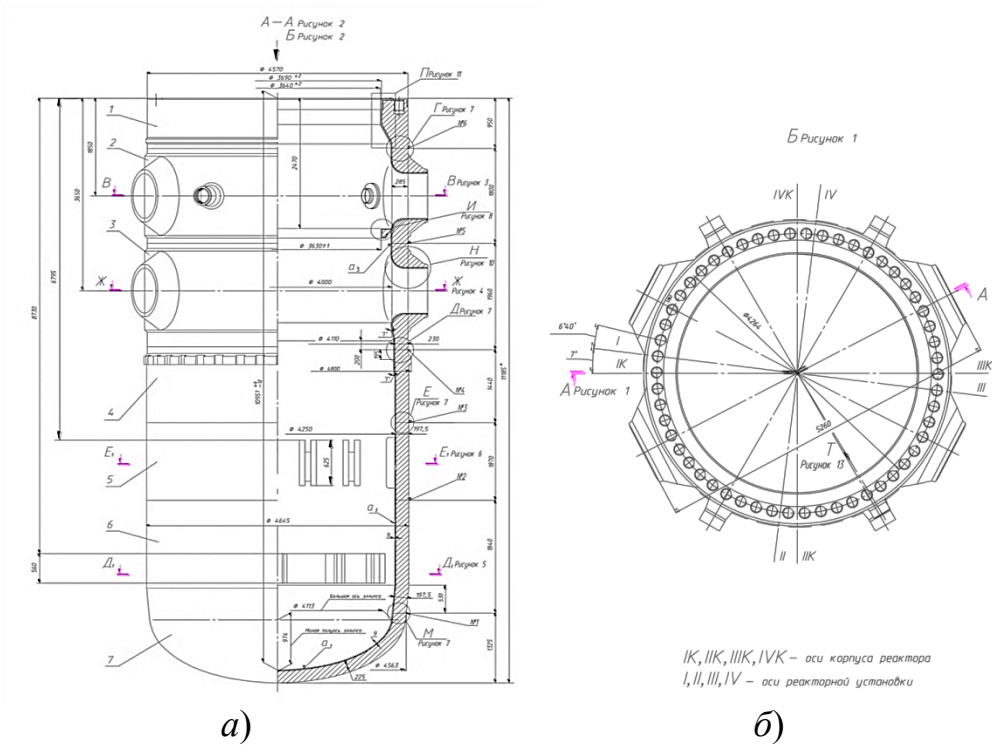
Корпус реактора ВВЭР-1200: а – вид сбоку, б – вид сверху
